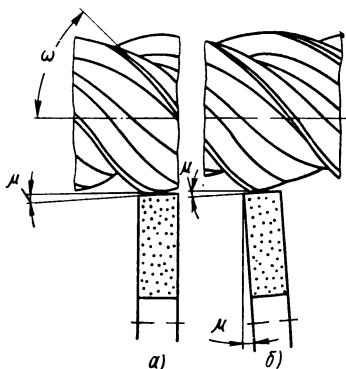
Схема шлифования по окружности цилиндрических фрез с большим углом наклона винтовых канавок
